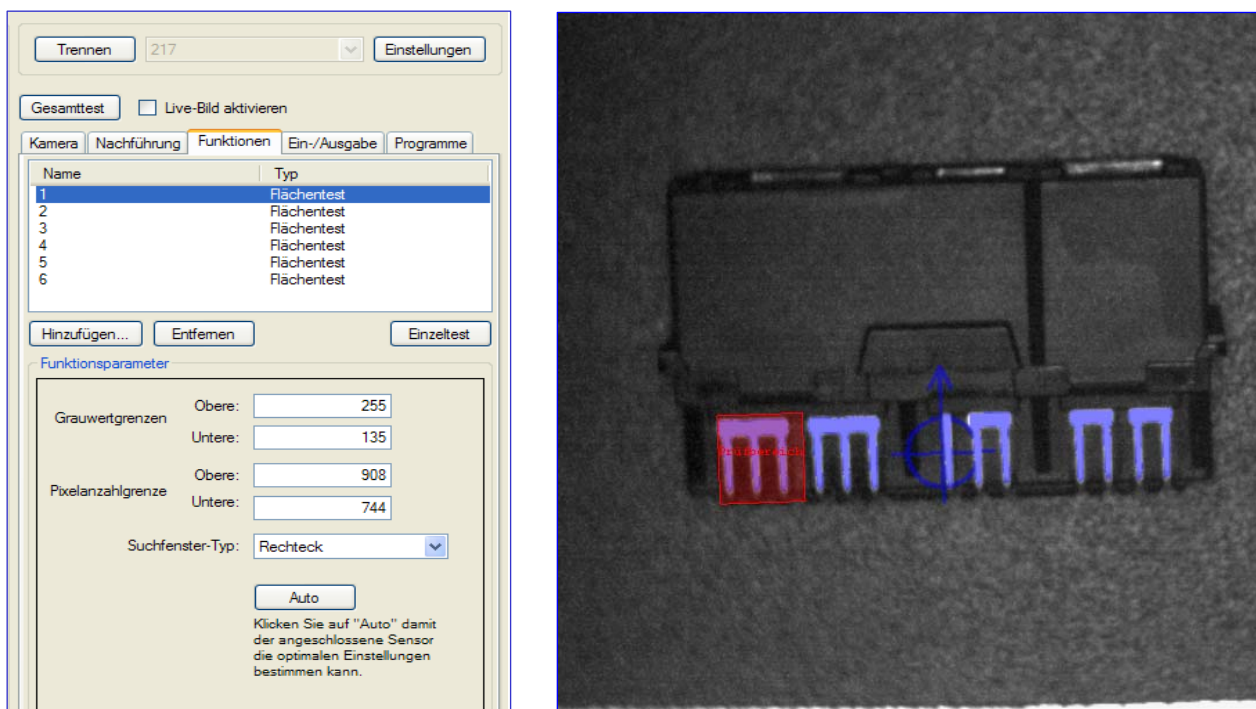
Prüfung einer Steckerleiste mit sechs Prüfbereichen und Lagenachführung
